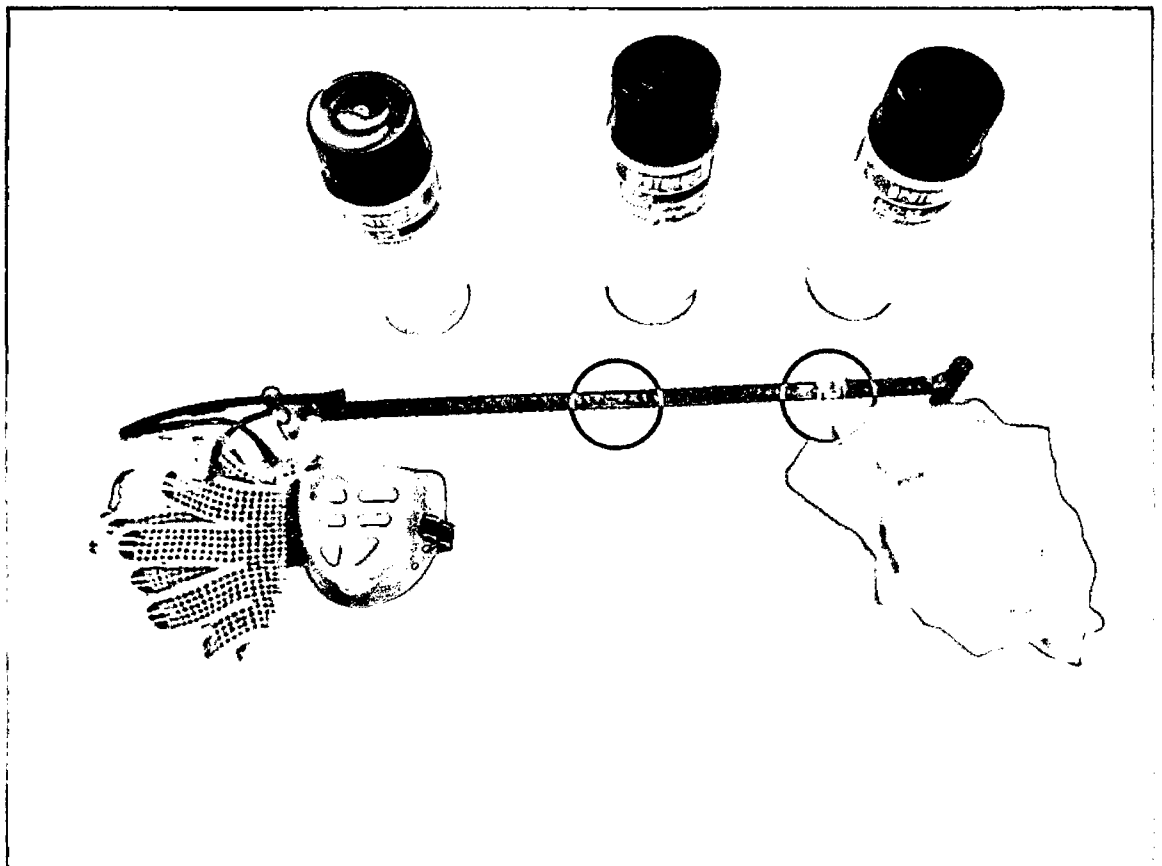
Equipo y materiales necesarios para le elaboración de la prueba por líquidos penetrantes.
